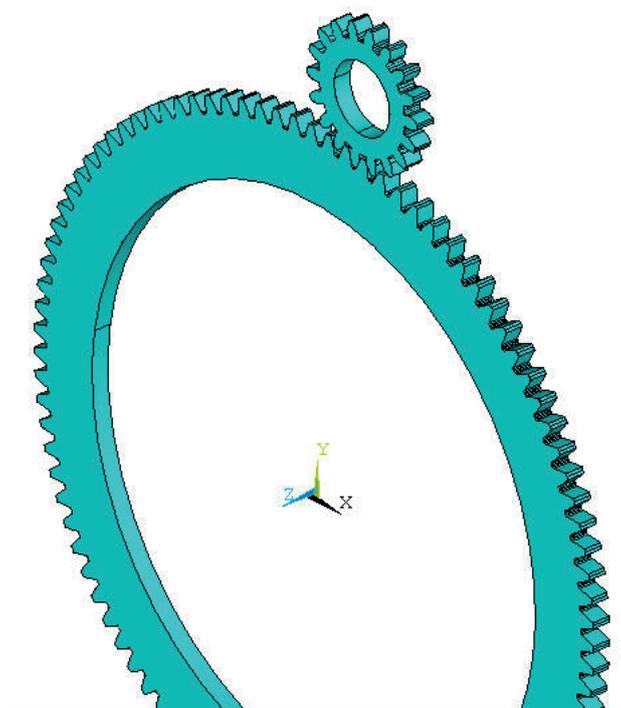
Геометрическая модель цилиндрической зубчатой передачи
